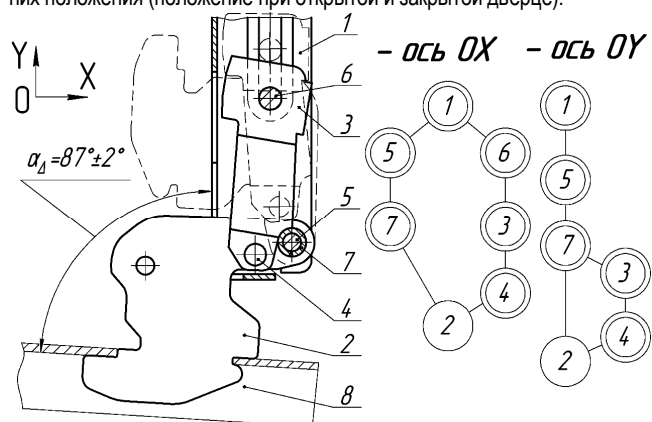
Эскиз сборочной единицы и графы деталей: 1 – корпус; 2 – тяга; 3 – кронштейн; 4 – ось тяги; 5 – ось; 6 – ось механизма; 7 – обойма; 8 – блок шарнира
